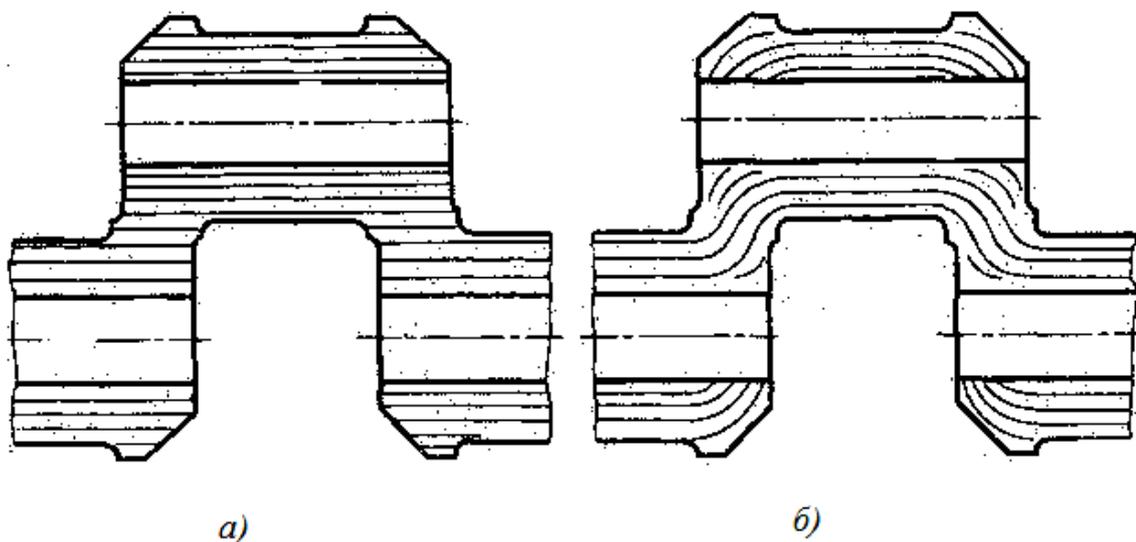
Расположение волокон коленчатых валов, полученных из сортового проката механической обработкой (а) и горячей ковкой (б)
